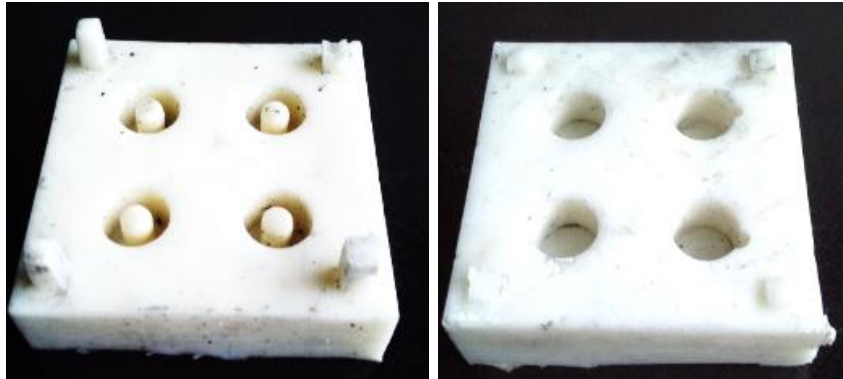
Moldes de caucho de Silicona, molde 1 (izquierda), molde 2 (derecha)
